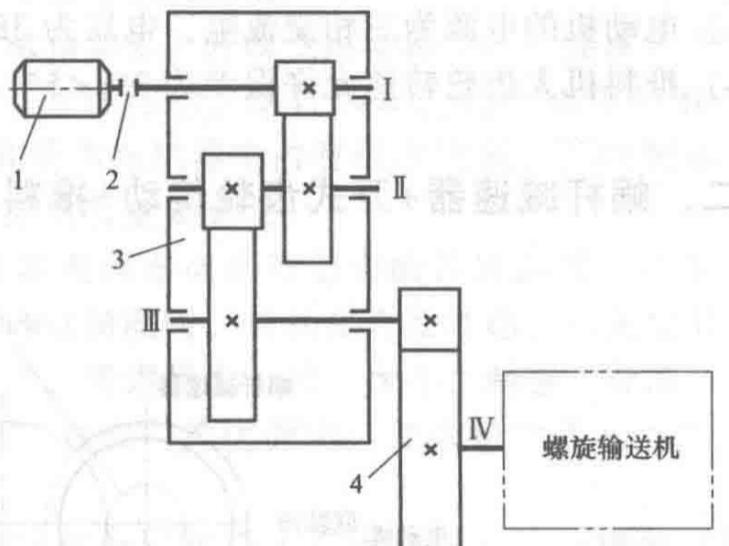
二级展开式圆柱齿轮减速器+开式齿轮传动
